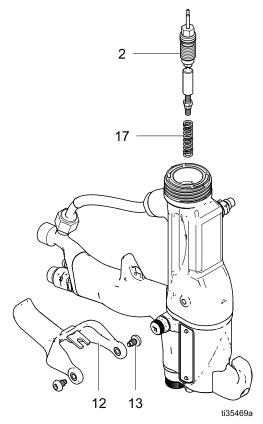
Desmontaje de la varilla de empaquetadura de fluido
